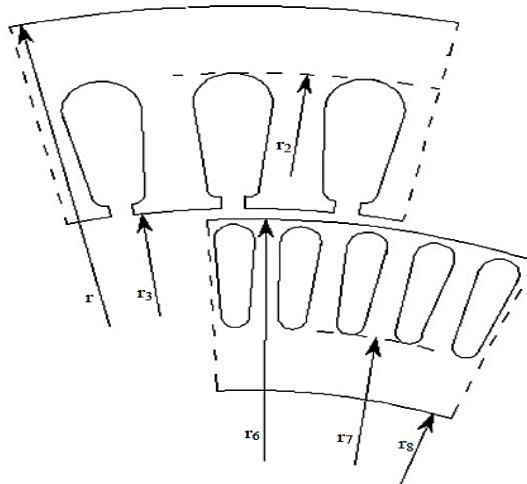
Dimensions principales du moteur asynchrone à cage
